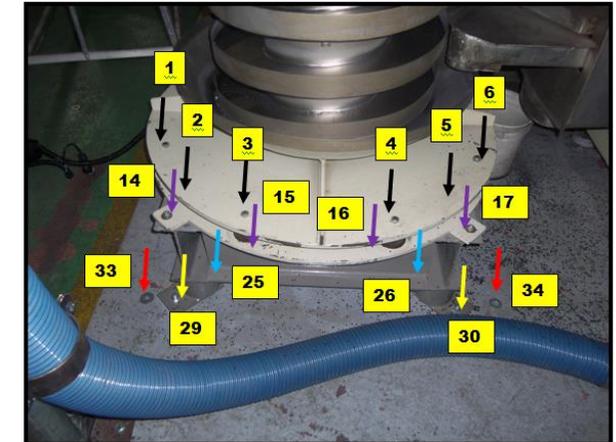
Pontos de Medidas – Estruturas e Piso – Elevador Vibratório
